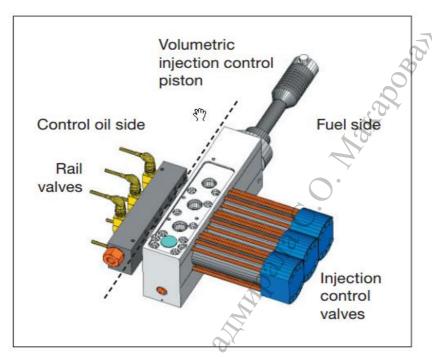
Rail Unit (RU) - Модуль впрыска «требуемого» количества топлива: Control oil side - Сторона «управляющего» масла, Rail valves (RV) - Клапаны впрыска из FR - топливной магистрали, Fuel side – «Сторона» топлива, Volumetric injection control piston (VICP) - Поршень контроля объема «впрыскиваемого» топлива, Injection control valves - Клапаны управления впрысками
